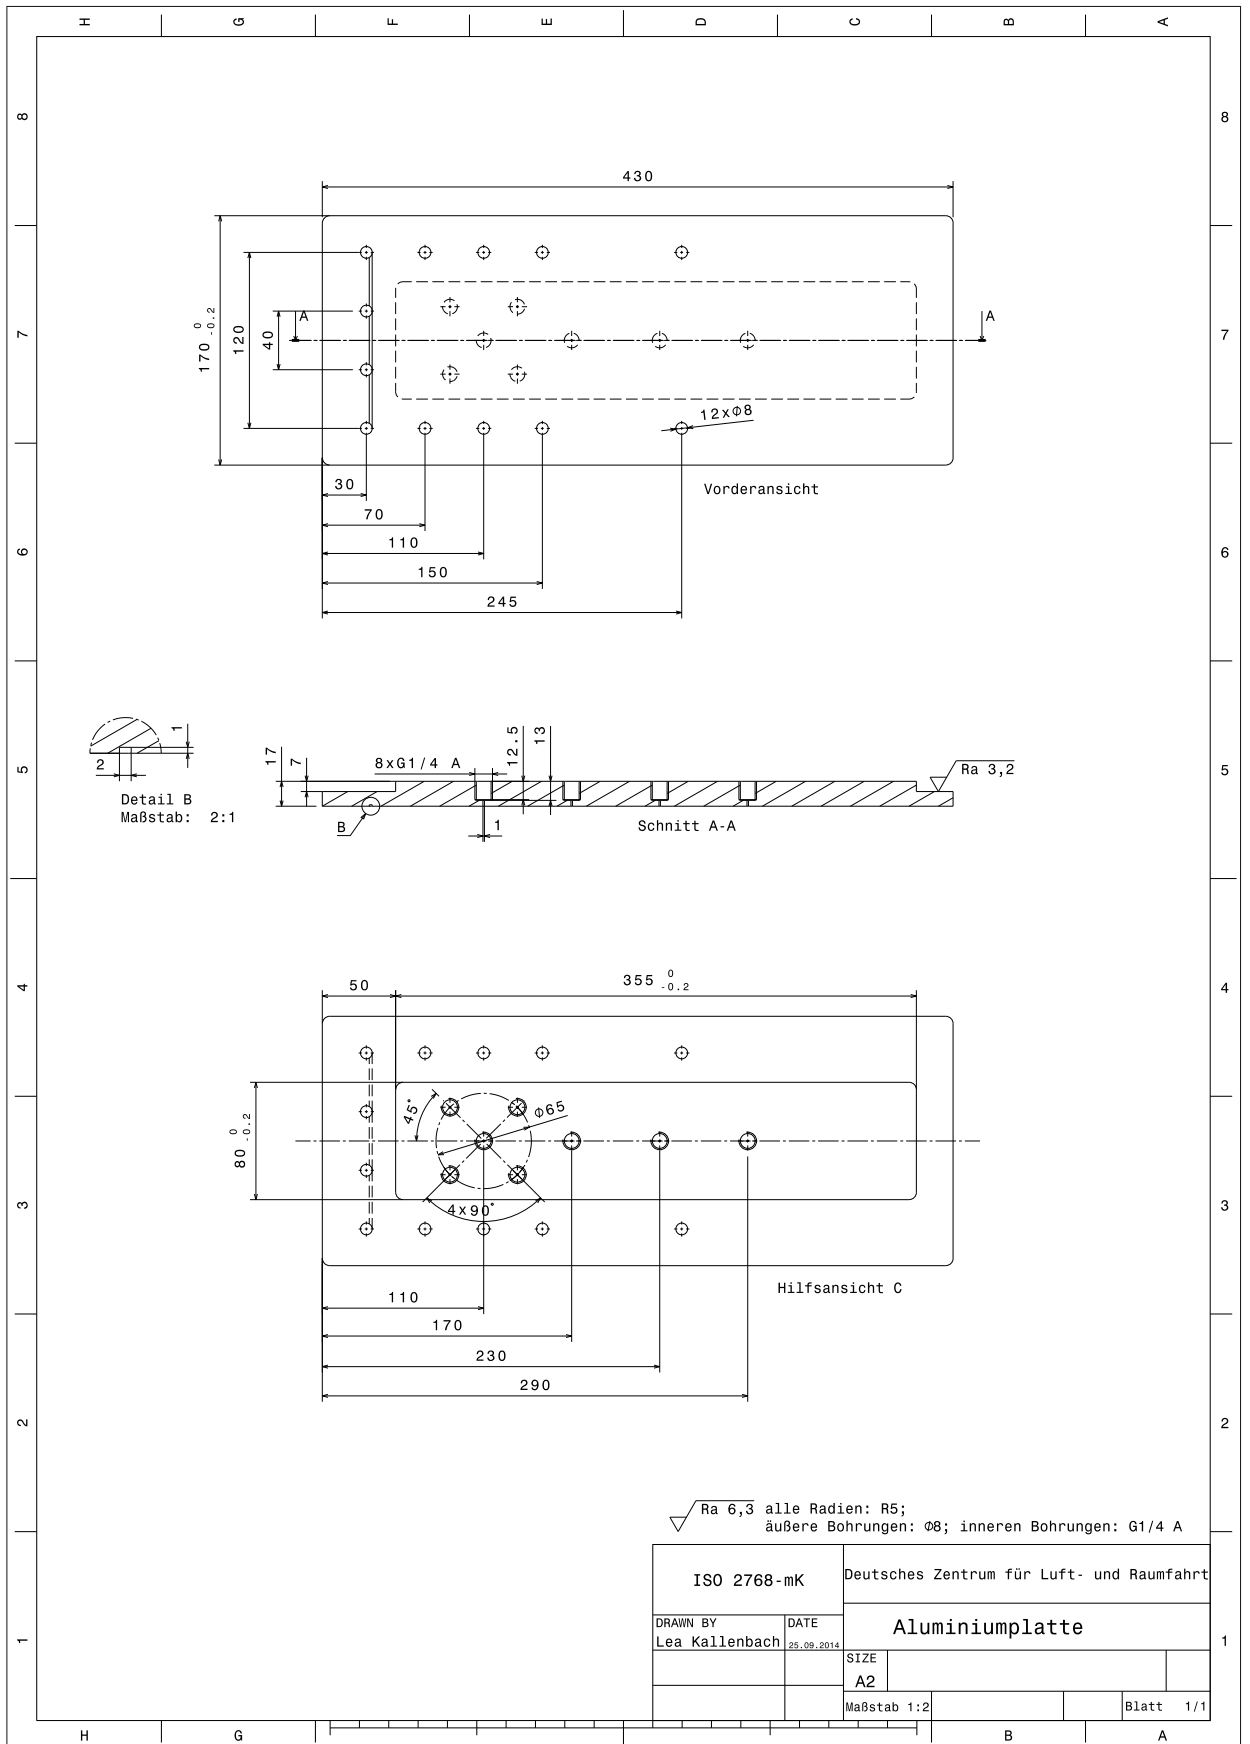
Aluminiumplatte für das RTM-Werkzeug
